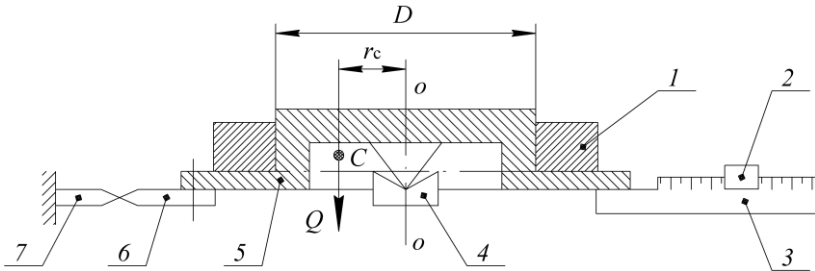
Схема статической балансировки на весах: 1 – балансируемая деталь; 2 – груз-компенсатор; 3 – линейка компенсирующего устройства; 4 – основание; 5 – платформа; 6 – подвижная стрелка; 7 – неподвижный репер
